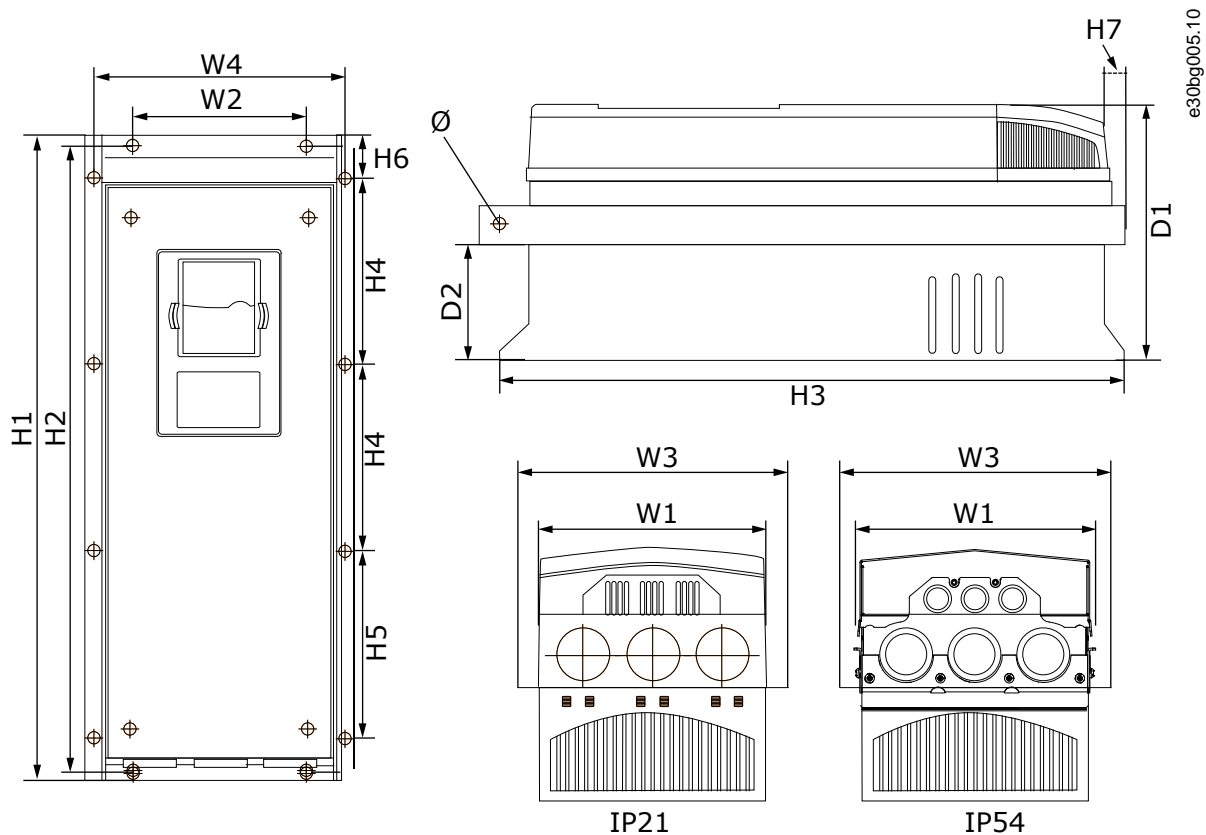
Abmessungen des VACON® NXS/NXP AC Drive mit Flansch, FR7–FR8
